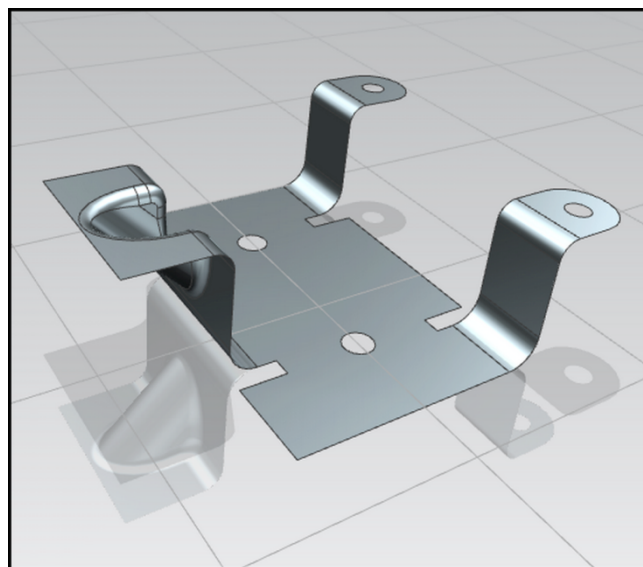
Листовое тело – наружная поверхность (по матрице) детали Support
